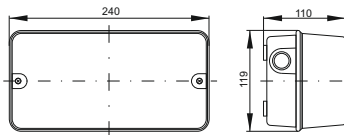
Габаритные и установочные размеры светильника НПП 3006
